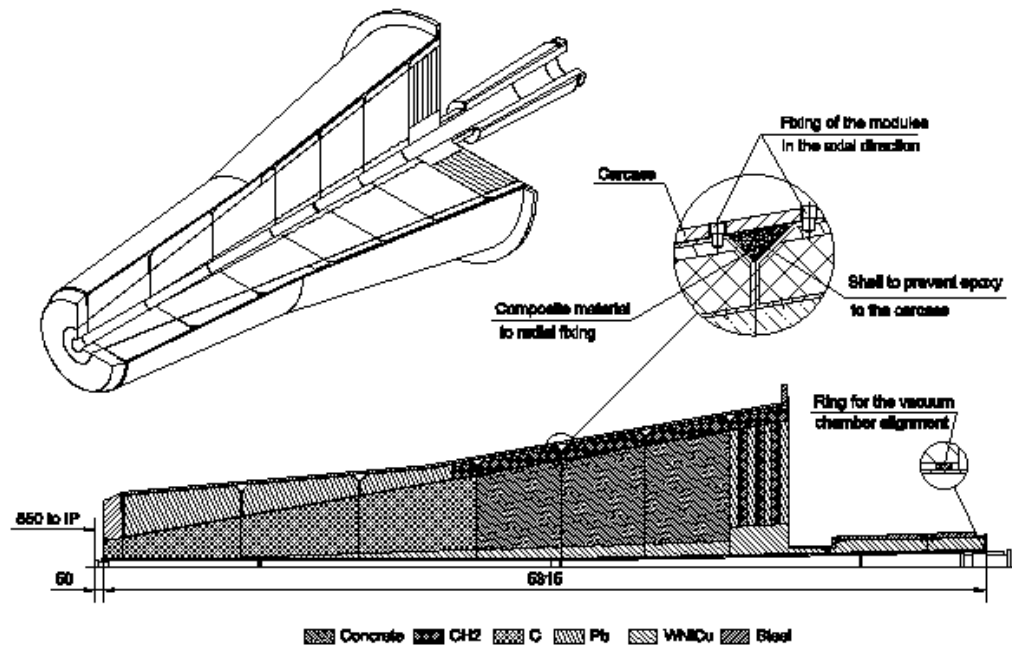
Vues en coupe de l'absorbeur frontal.
